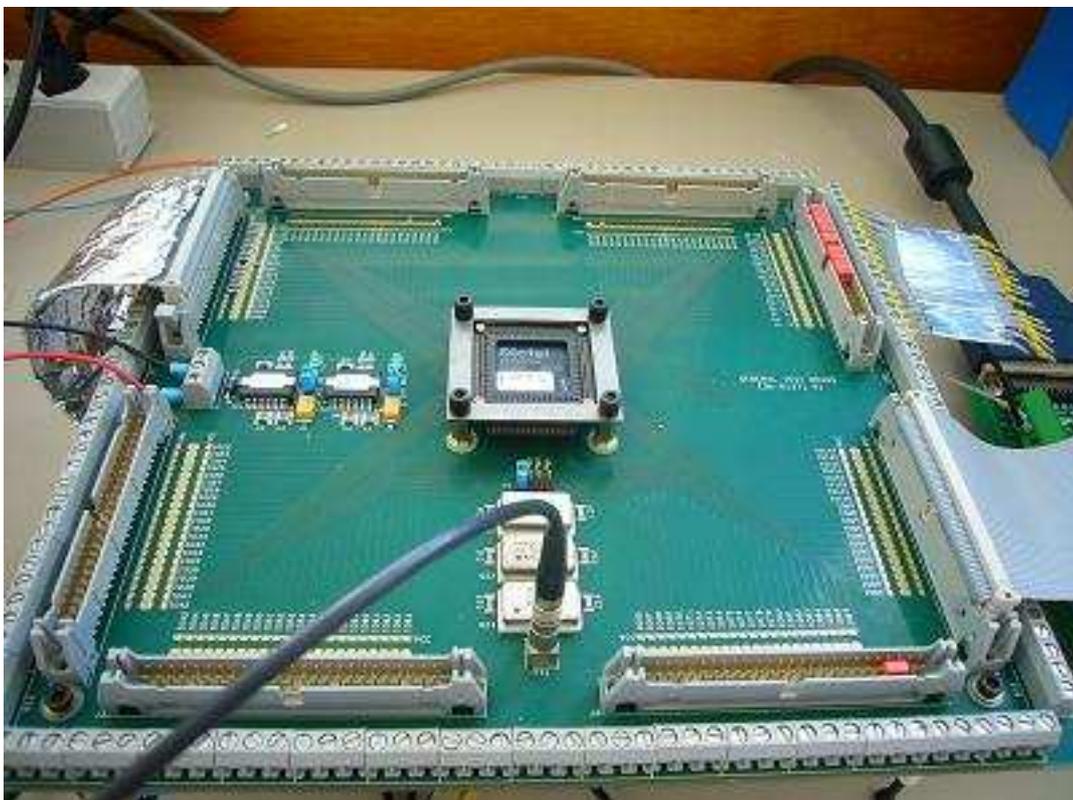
Carte électronique (PCB) pour le CI. Le support est soudé au centre.
